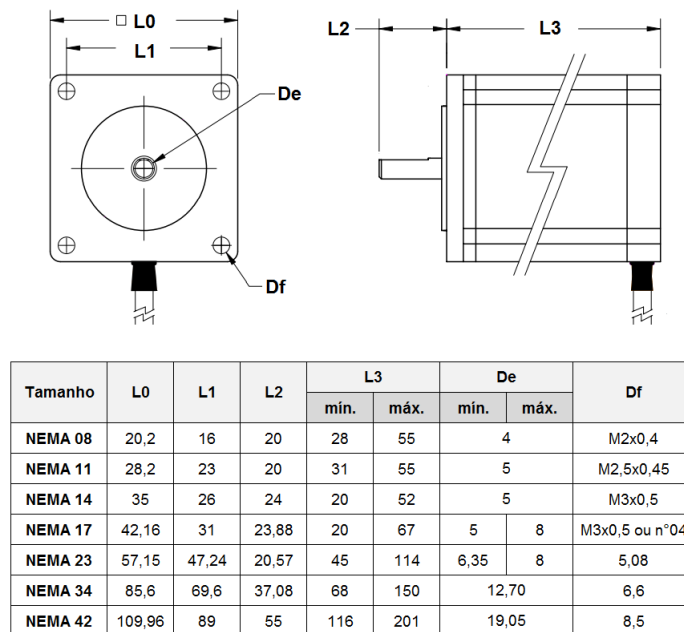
Principais dimensões de um motor de passo (em milímetros).
